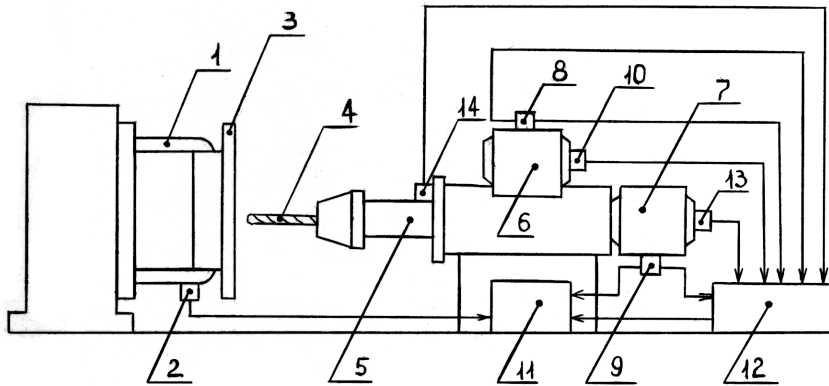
Структурная схема экспериментальной установки контроля износа сверл: 1 – кулачок зажимного устройства; 2 – пьезоэлектрический виброизмерительный датчик; 3 – обрабатываемая деталь; 4 – сверло; 5 – шпиндель; 6 – двигатель подачи шпинделя; 7 – двигатель вращения шпинделя; 8, 9 – датчики измерения активной мощности, потребляемой двигателями; 10 – датчик скорости вращения двигателя подачи; 11 – блок контрольно-измерительных регистрирующих приборов; 12 – устройство управления процессом сверления на базе программируемого контроллера
